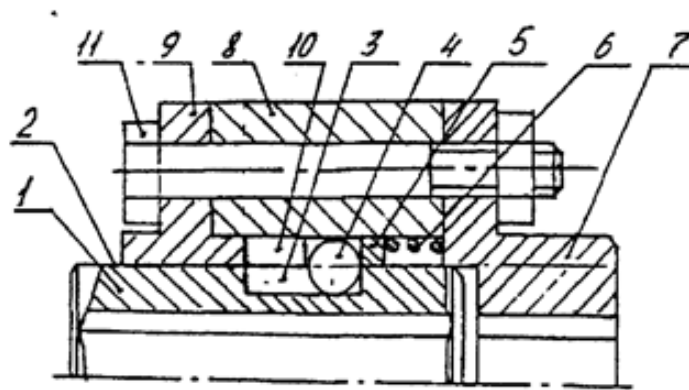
Конструкція запатентованої кулькової обгінної муфти з циліндричними поверхнями напівмуфт
